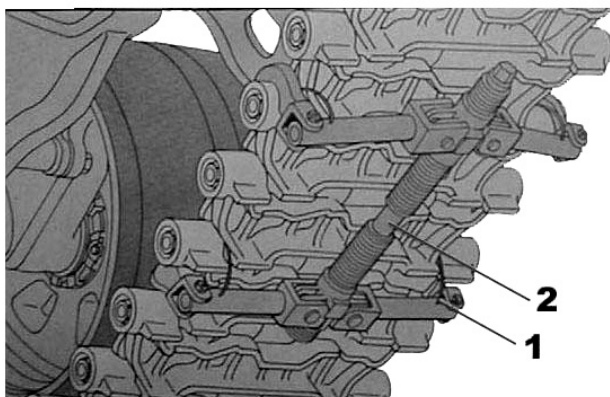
Приспособление (стяжка) для соединения гусеницы: 1 – петли; 2 – винт
